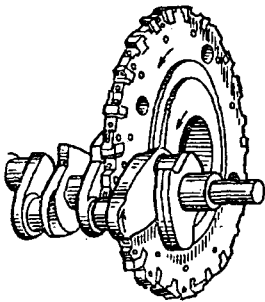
Ротаційне фрезерування шатунних шийок колінчастого валу.
